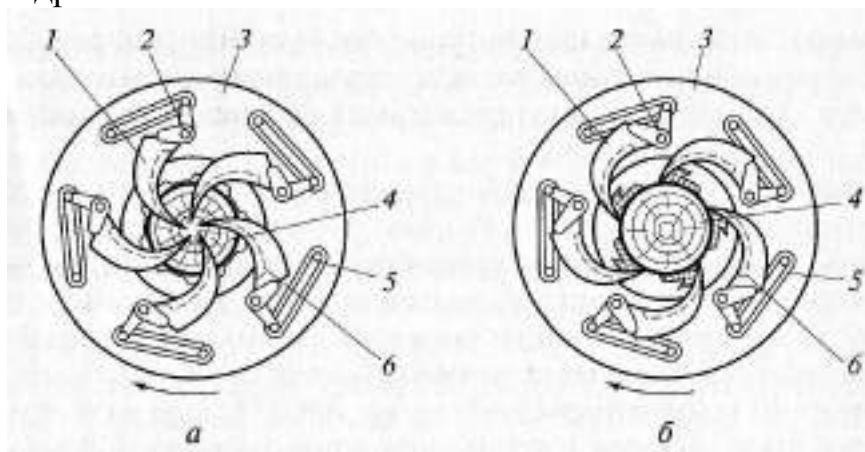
Схемы короснимающего механизма роторного окорочного станка с прижимом короснимателей резиновыми кольцами:
